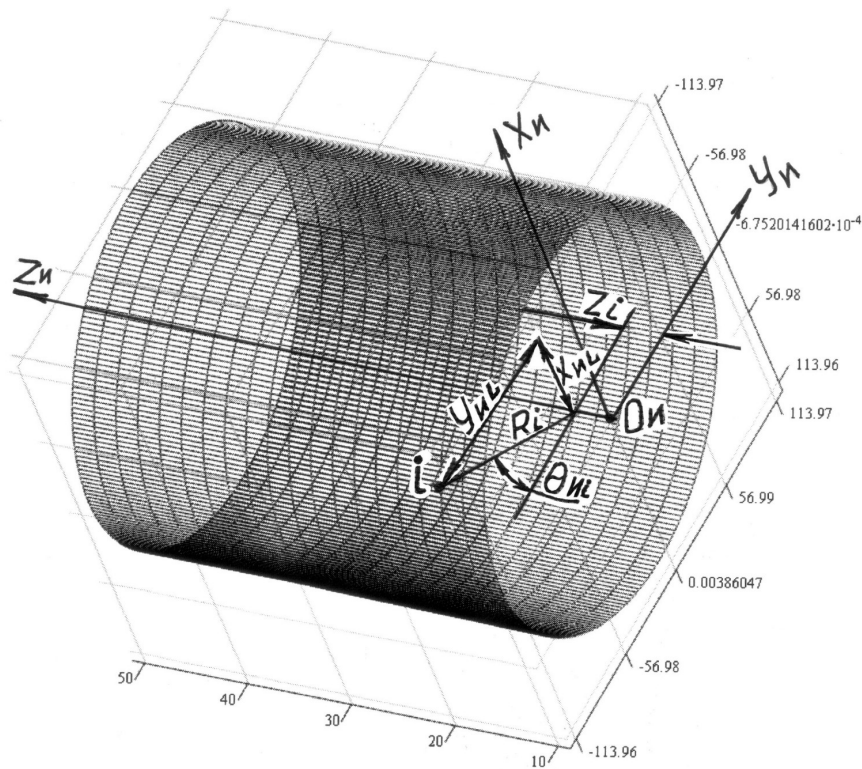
Робоча поверхня шліфувального круга, яка розрахована по 3D моделі (8, 9)
